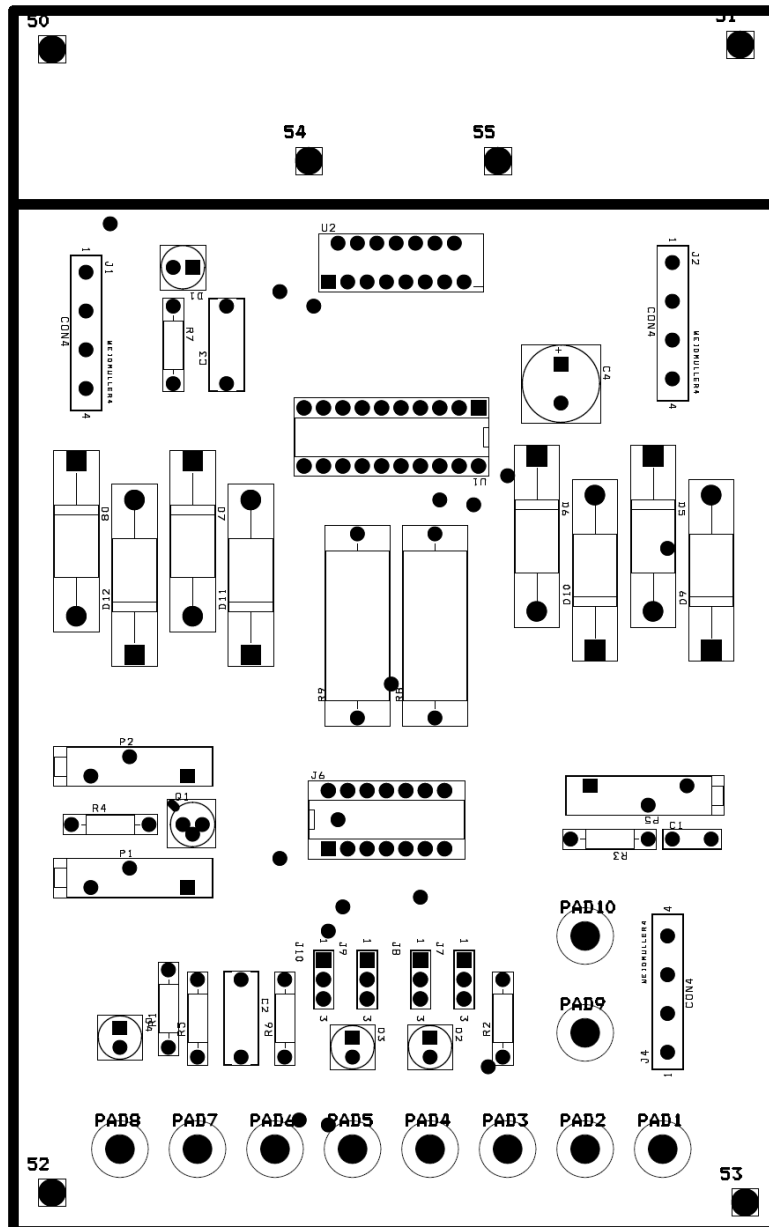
Capa de perforacions (DRL) de la PCB de la interfície per al motor bipolar
